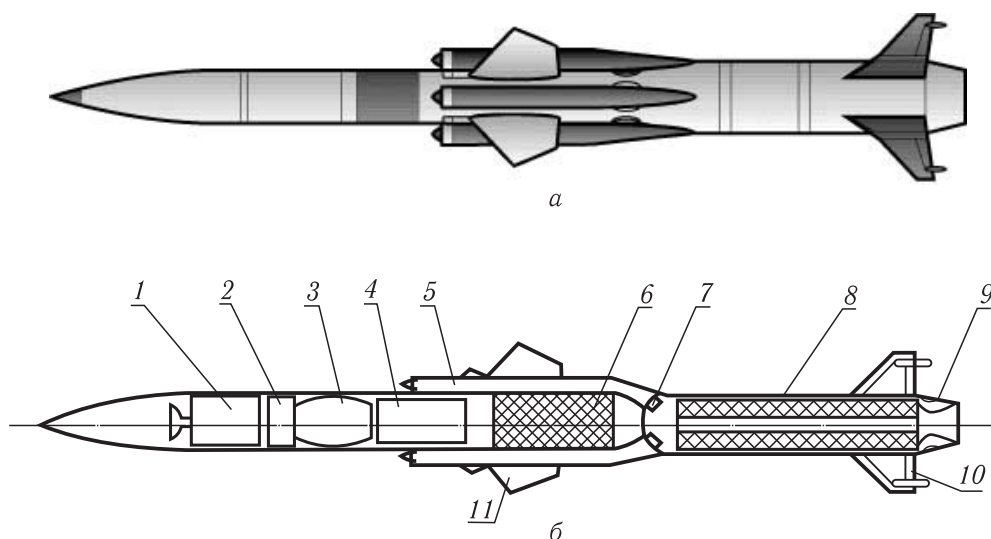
Внешний вид (а) и схема (б) ракеты ЗМ9 с ИРПДТ: 1 — блок управления, 2 — радиовзрыватель, 3 — боевая часть, 4 — автопилот, 5 — воздухозаборник, 6 — газогенератор с маршевым зарядом, 7 — заглушка; 8 — ТРТ разгонного РДТТ, размещаемый в камере сгорания; 9 — сбрасываемое сопло стартового режима, 10 — стабилизатор, 11 — крыло
